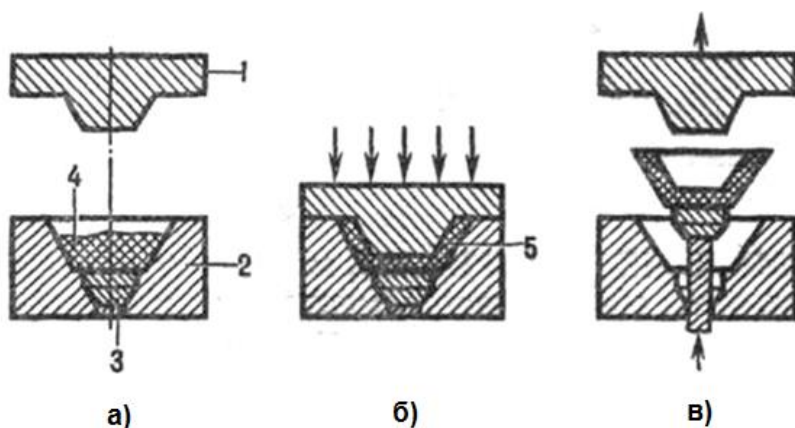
Прямое прессование: а-загрузка; б-прессование; в - выталкивание; 1-пуансон; 2-матрица; 3- выталкиватель; 4- прессматериал; 5- готовая деталь.
